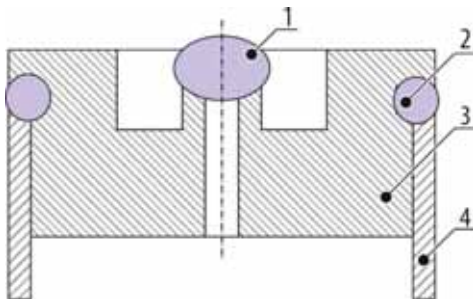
Конструкция заглушки с торцовым швом: 1 — первый сварной шов; 2 — второй сварной шов; 3 — заглушка; 4 — оболочка
